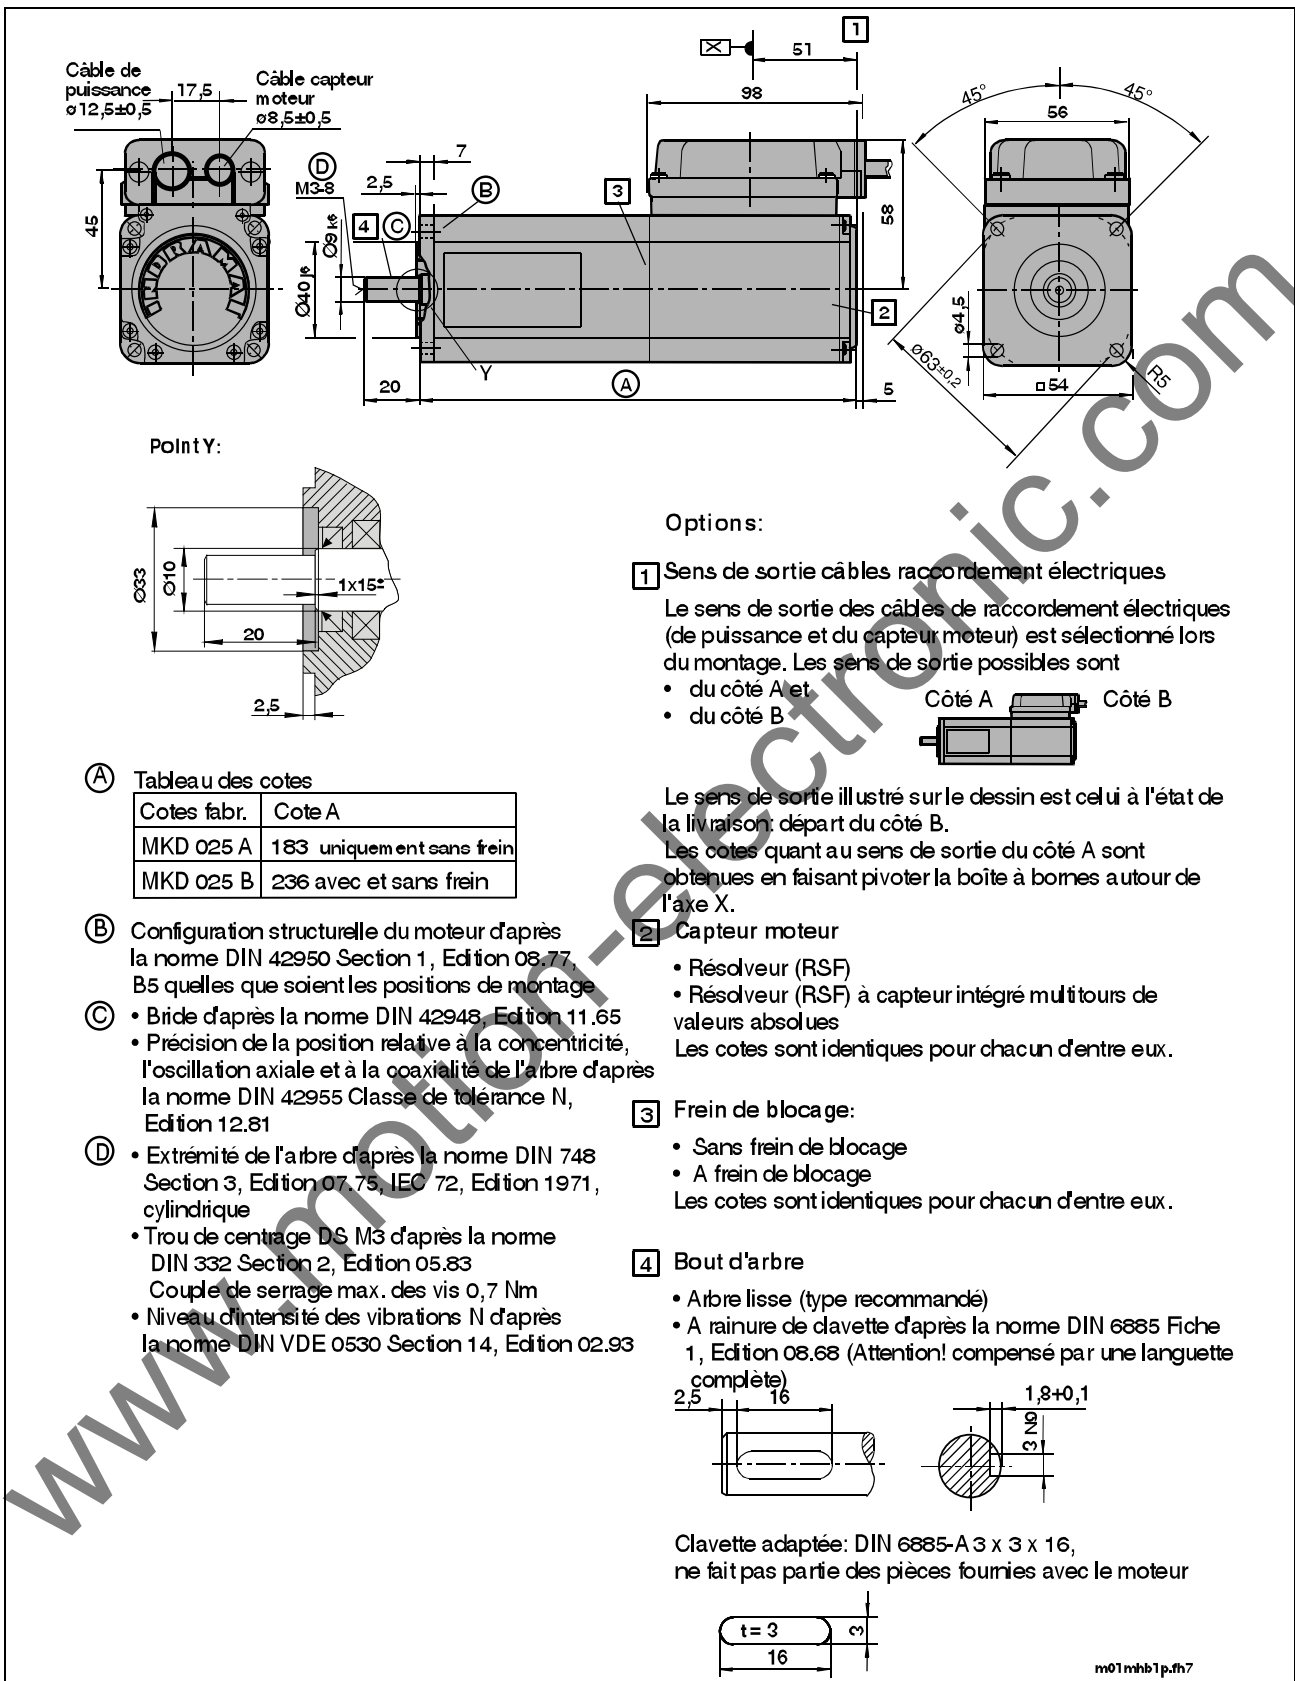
Fiche technique des moteurs MKD025A, MKD025B
